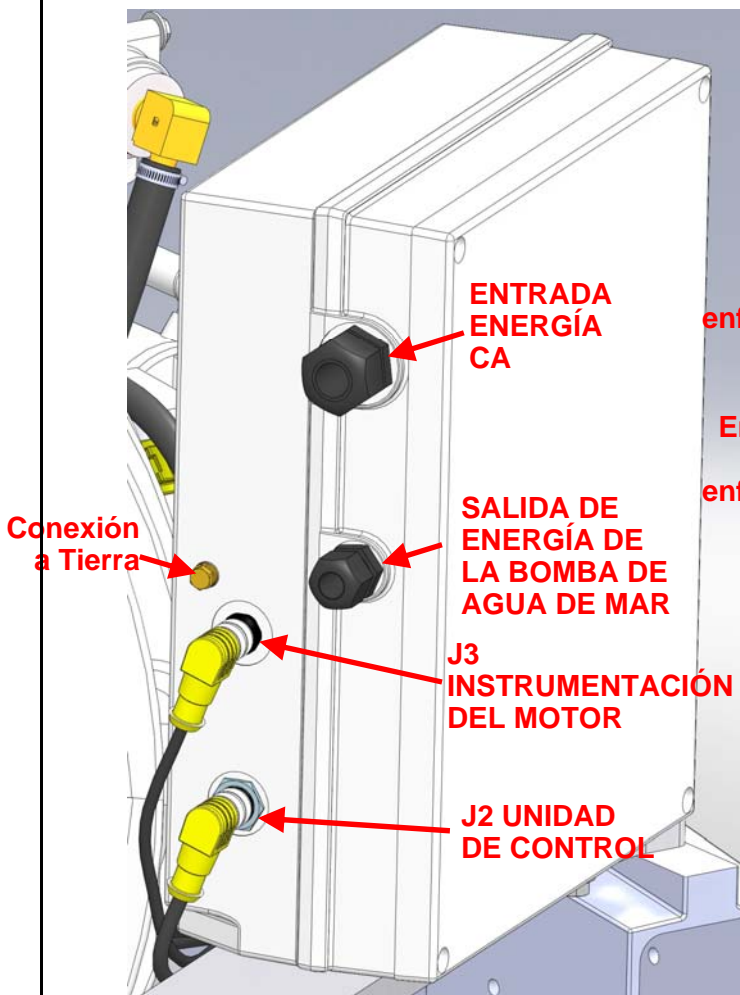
CONECTORES DE LA CAJA COMPACTA DE ACCIONAMIENTO POR MOTOR (LADO IZQUIERDO)
